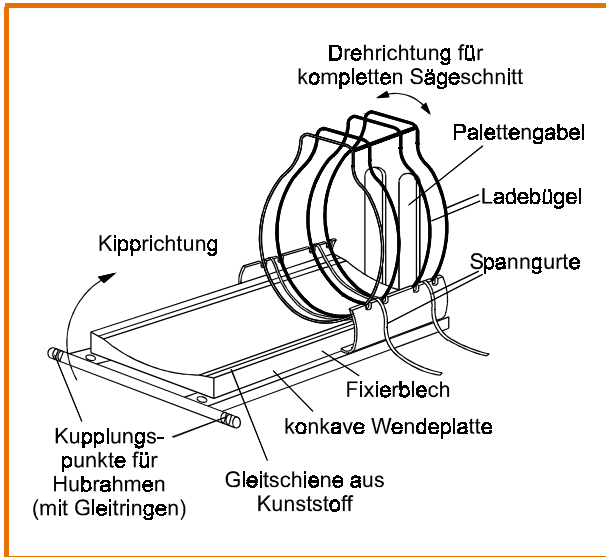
Stückholzbindeapparat, hier mit Wendepalette für einen Schlepperanbau-Hubrahmen (nach IBW /3-21/)
